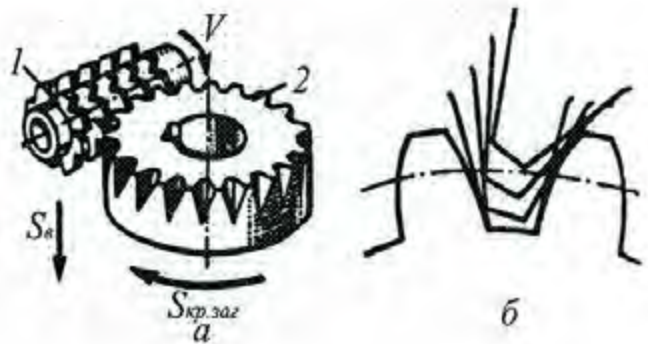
Схема формоутворення зубців циліндричного колеса черв'ячною фрезою за методом обкатування
